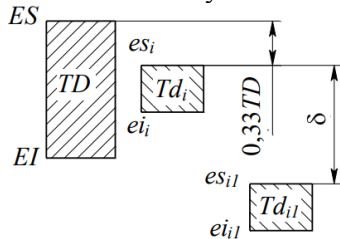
Схема розташування допусків отвору і розвертки
